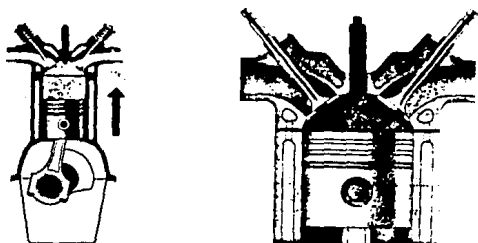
(a)Compresión del aire. (b)Cámara de combustión.
